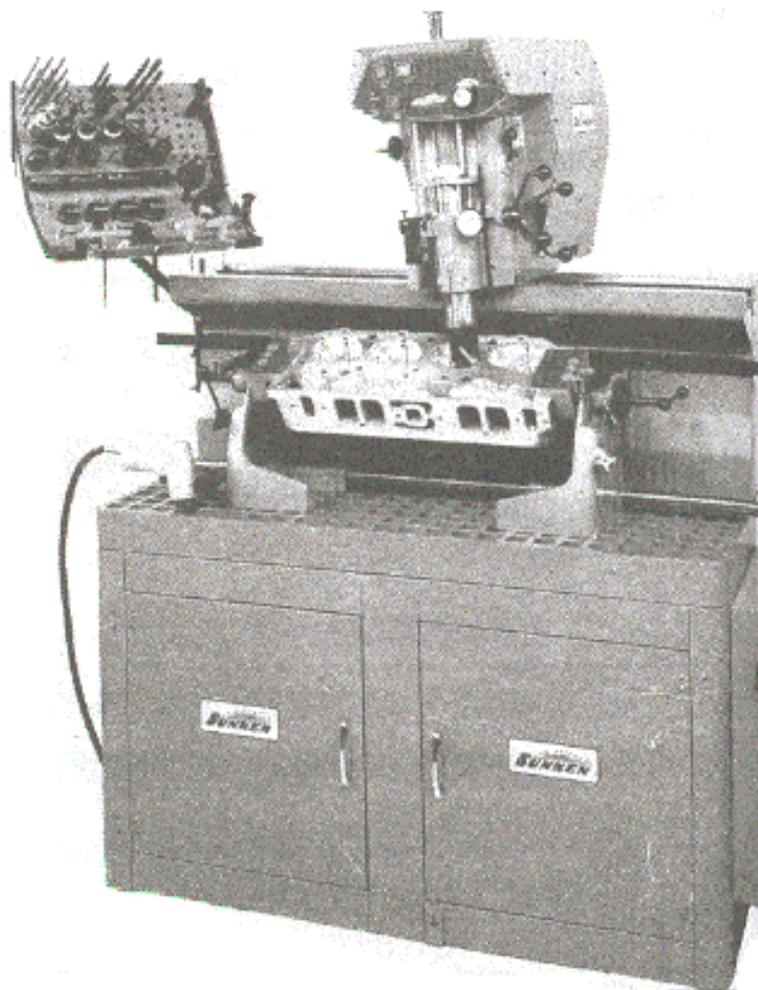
Станок для комплексного ремонта головок цилиндров SUNNEN
